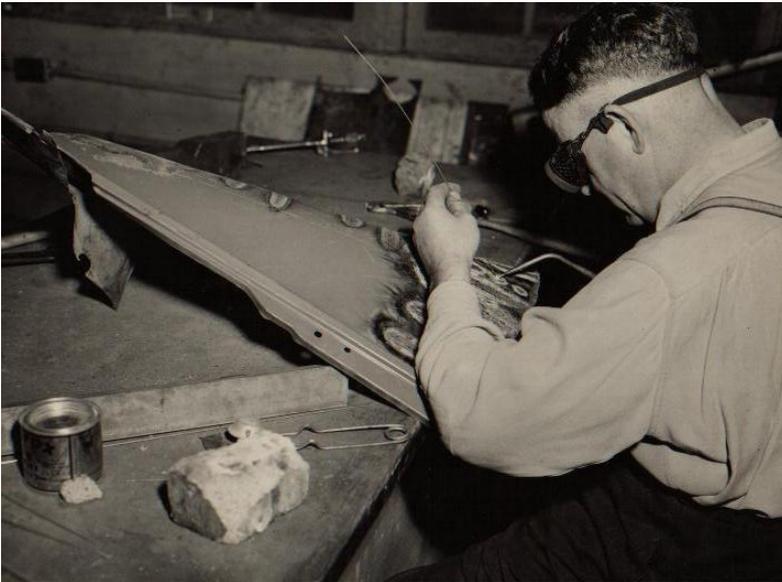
soldadura oxiacetilénica (reparación de chasis), 1949
